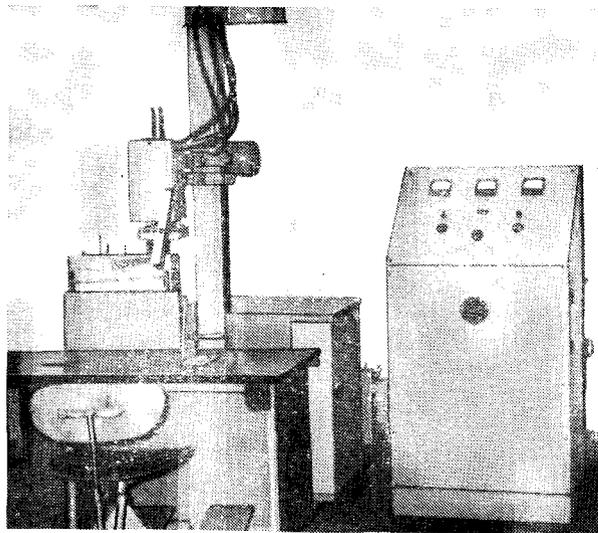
Ультразвуковая сварочная машина КТУ-1,5
